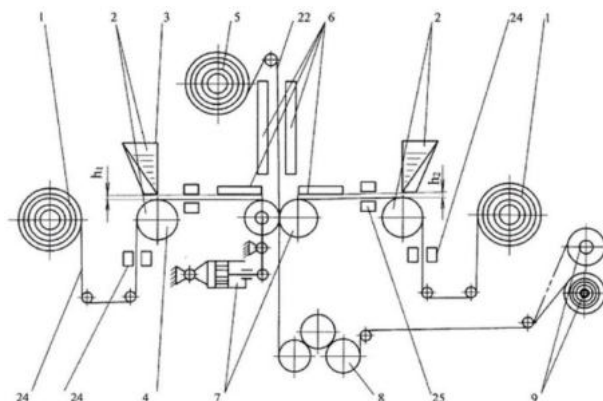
Установка для изготовления пленочных клеев и клеевых препрегов конструкционного назначения
